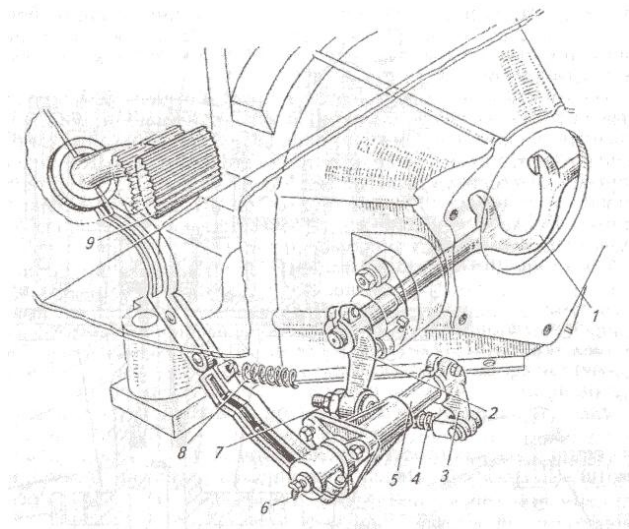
Привод сцепления автомобиля ЗИЛ-431416: 1 - вилка выключения сцепления; 2 - рычаг; 3 - промежуточный рычаг; 4 - тяга; 5 - вал педали; 6 - маслёрка; 7 - сферическая гайка; 8 - пружина; 9 - педаль.
